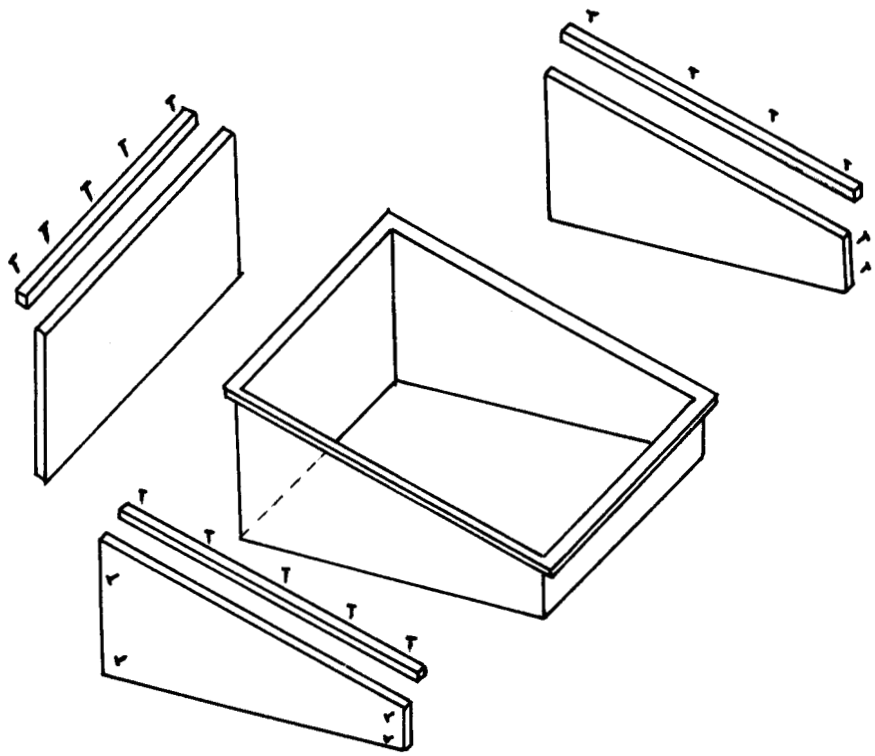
PROCESO DE MONTAJE DE LAS PARTES DEL MOLDE DE MADERA DE LA ESTRUCTURA EXTERNA DEL D.S.C.
